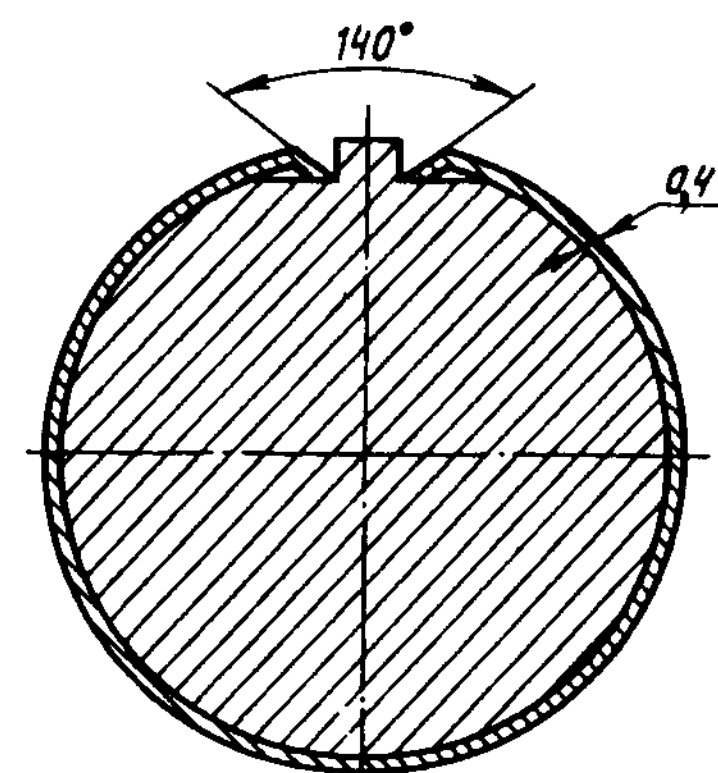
Схема установки упругой ДРД на шейку вала
